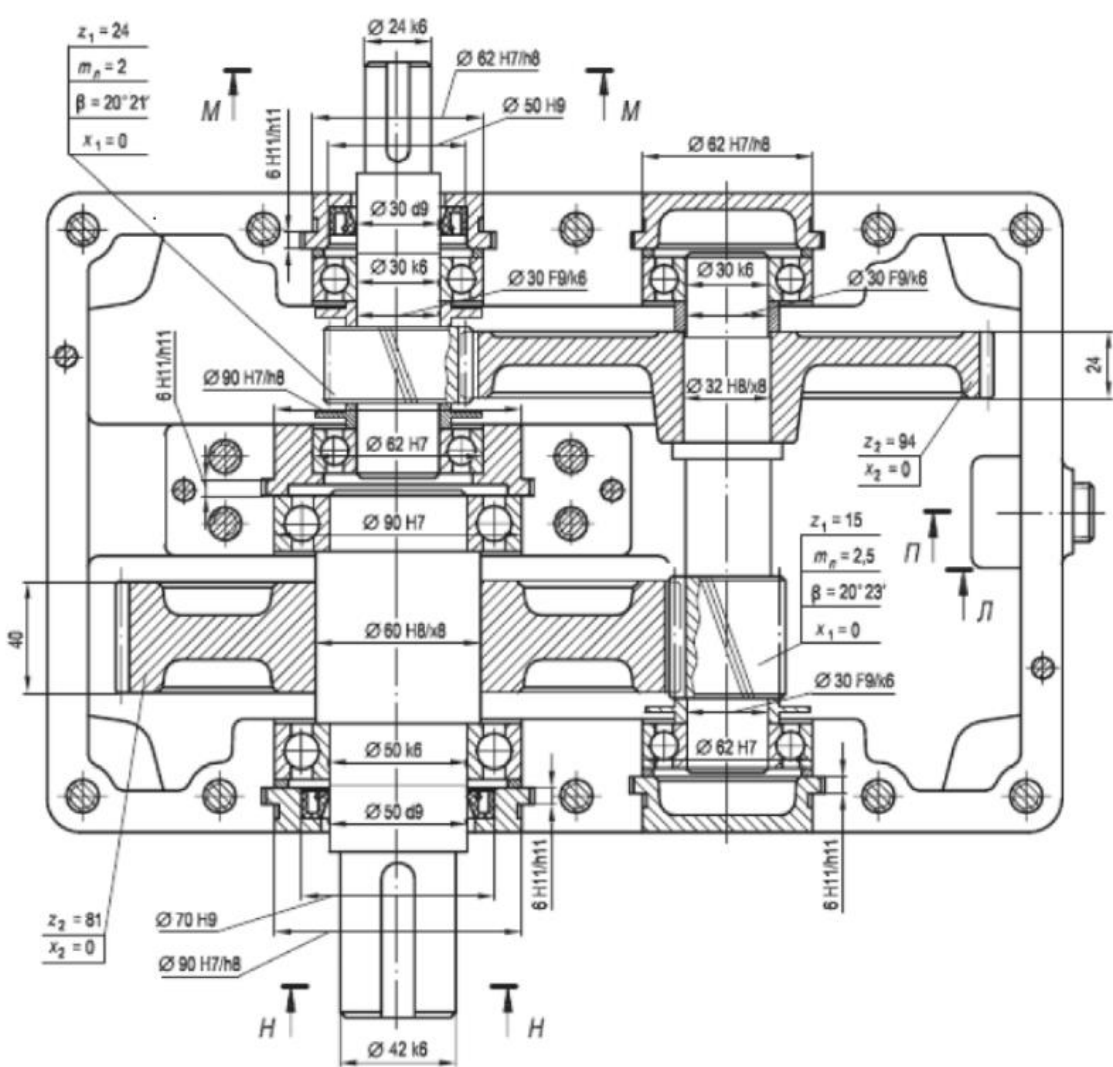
Редуктор двухступенчатый цилиндрический соосный
